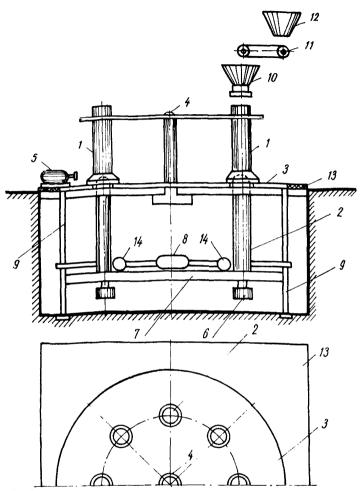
Схема многогнездного станка для изготовления труб спосо-
